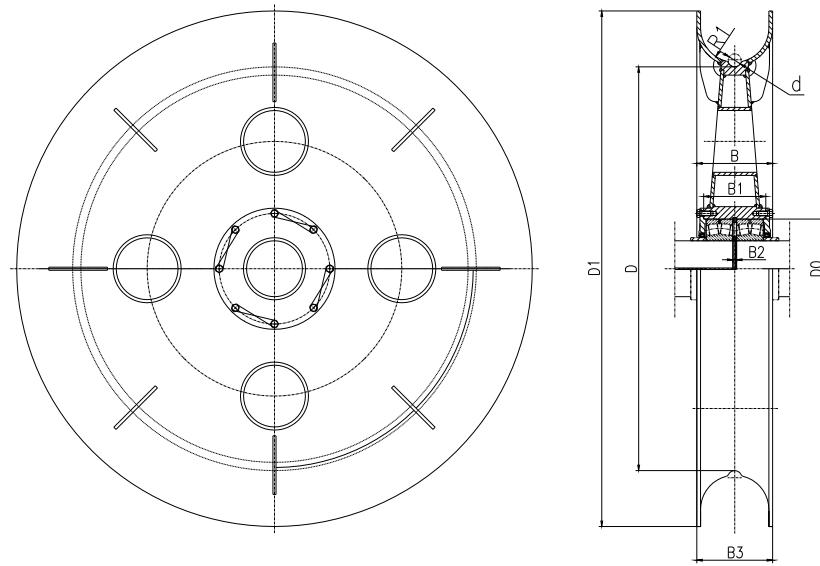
宽槽焊接滑轮 Fig. 6 Wide groove welded sheave
